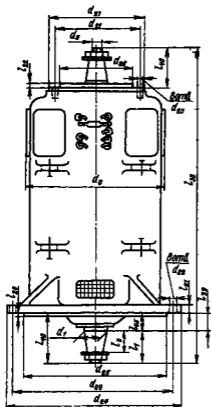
9 Габаритные и установочно-присоединительные размеры экскаваторных двигателей вертикального исполнения
